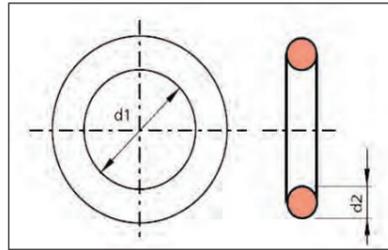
Ausführung von FEP-ummantelten O-Ringen
